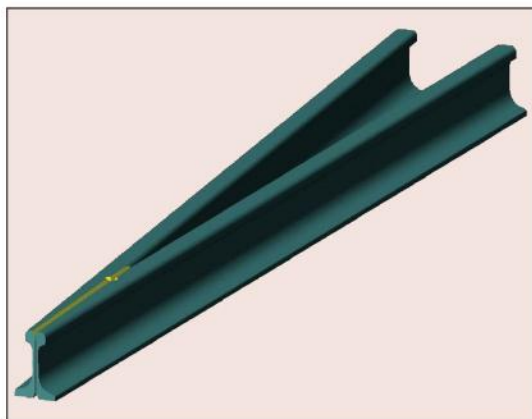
Внешний вид сварного шва со стороны головки рельса
